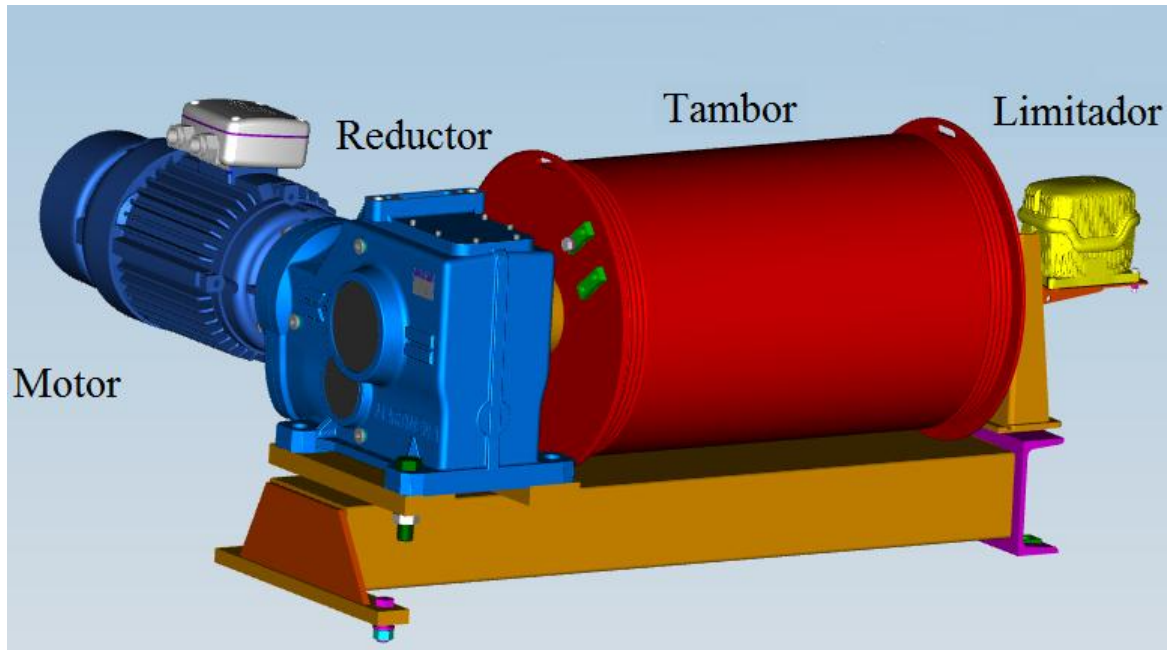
Mecanismo de carro con tambor de enrollado de cable
